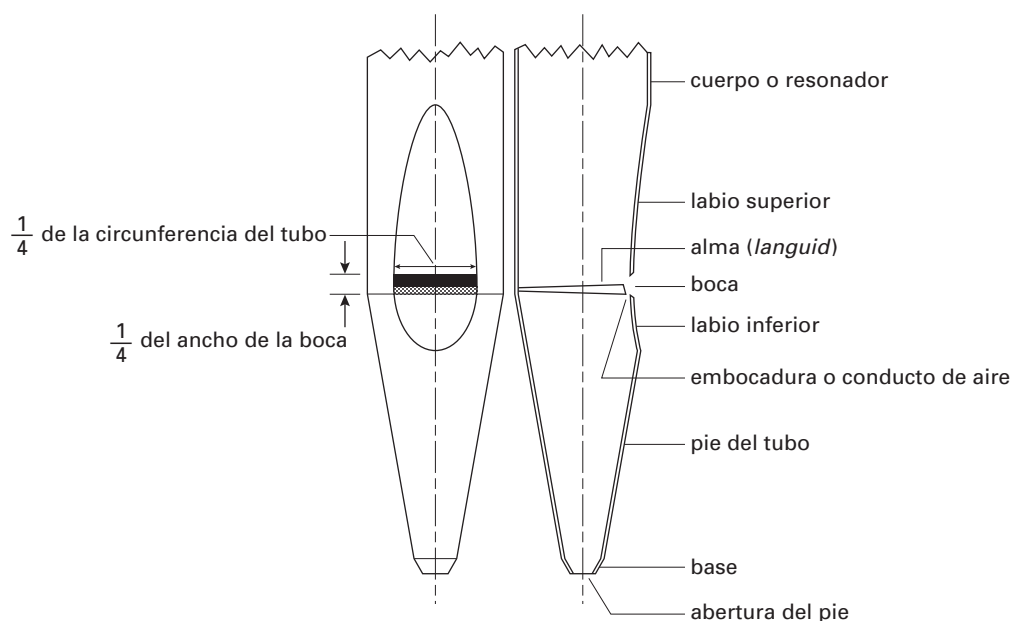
Tubo de boca o labial (flautado); vista frontal y transversal.
